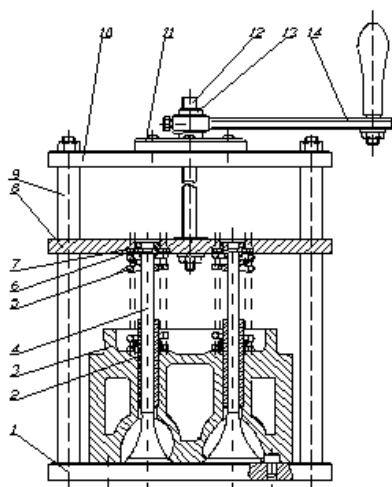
Схема приспособления для разборки головок автомобиля КамАЗ–740 (обозначение в тексте)
